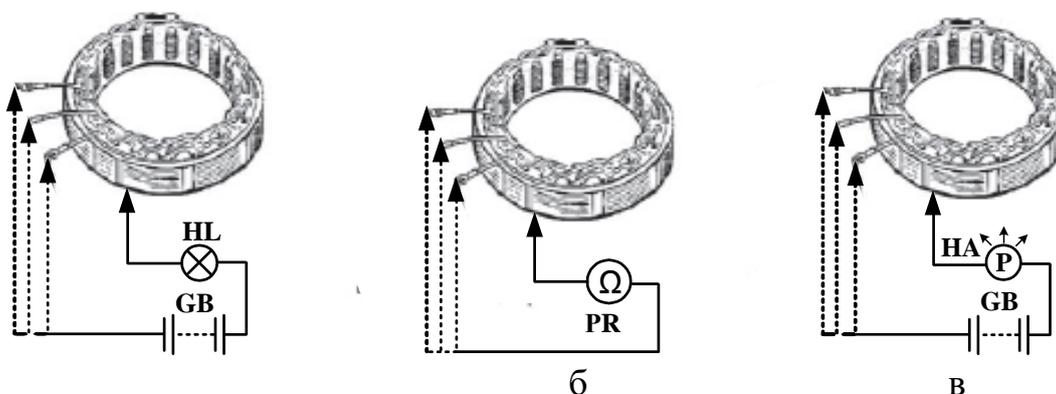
Схема проверки статорной обмотки на замыкание с корпусом ротора
